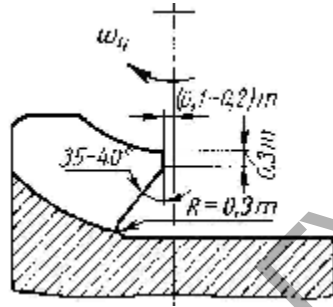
Конструктивное усовершенствование червячного колеса [37]
